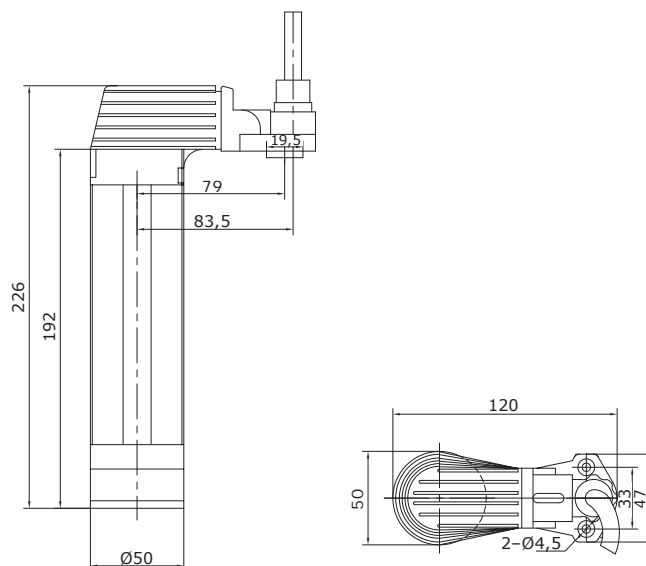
Габаритные размеры магнитного поплавки APV.M.06.32.03.AV1
